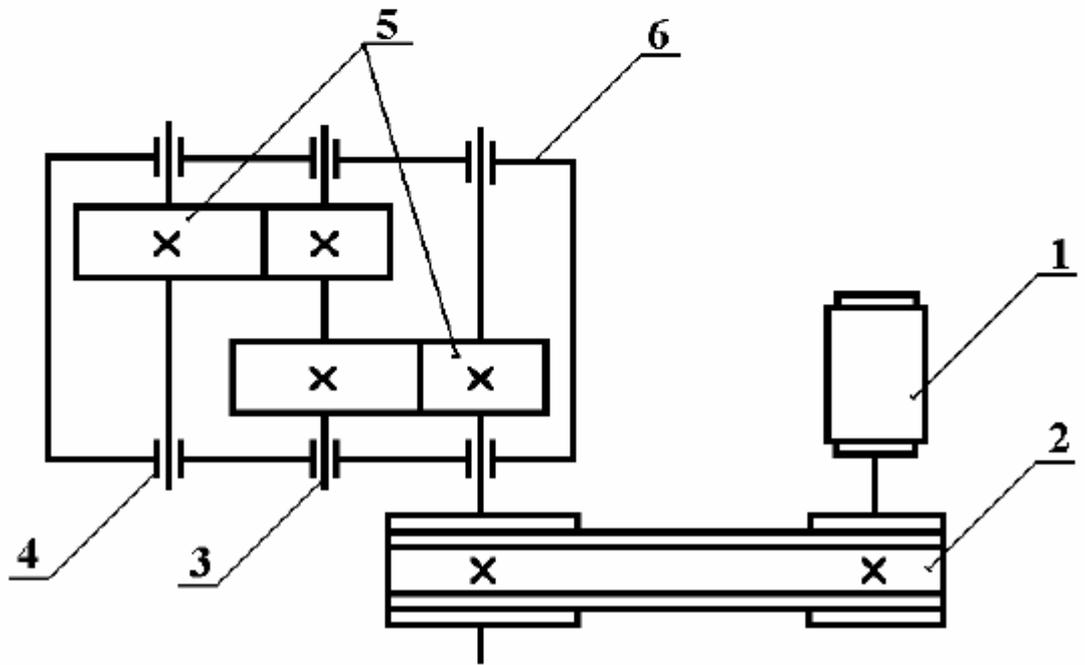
Кинематическая схема привода с зубчатым редуктором
